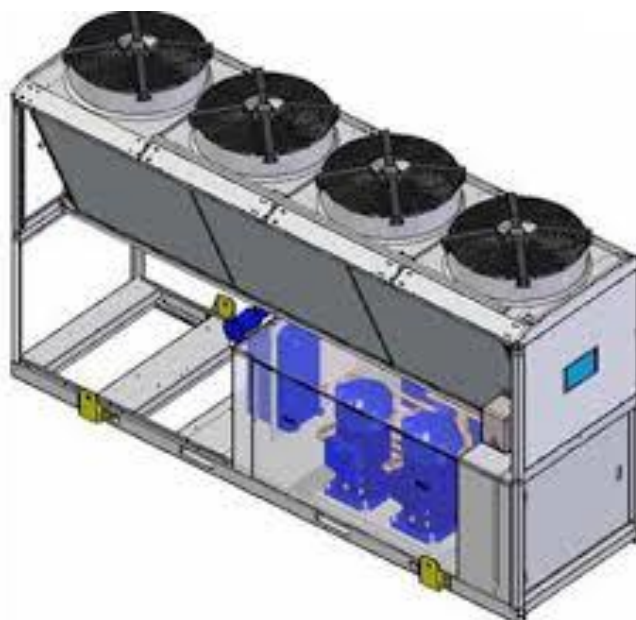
Загальний вигляд агрегату компресор-конденсатор для чилера
